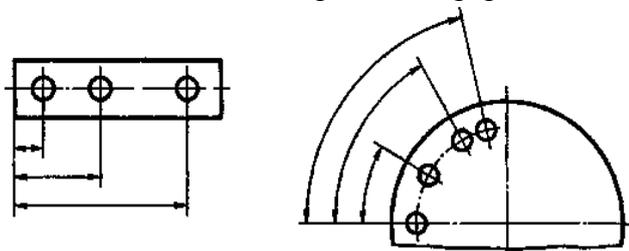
Координатный способ нанесения размеров от одной, основной базы
